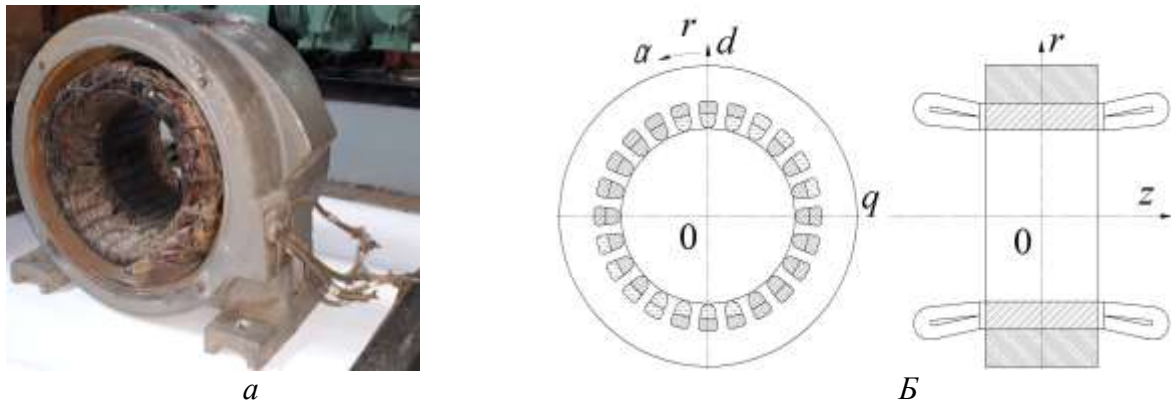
Індуктор ЕМПСР: а – зовнішній вигляд; б – конструктивна схема
